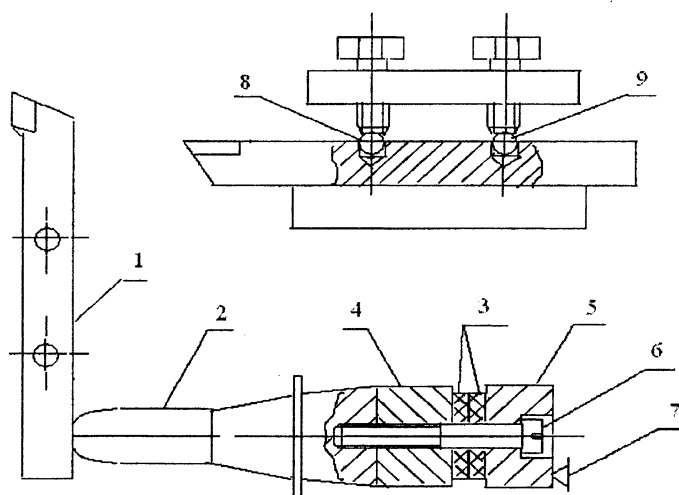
Схема установки системы инструмент–акустический преобразователь
